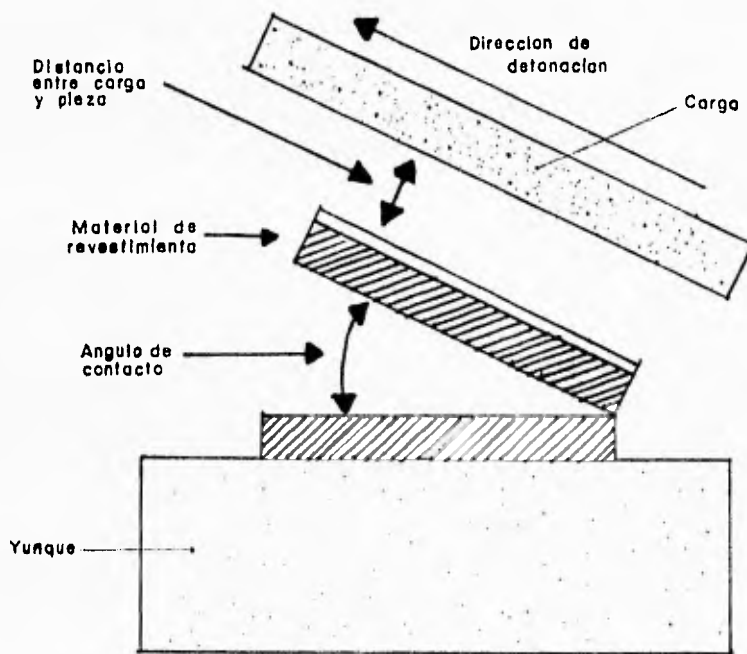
Soldadura por explosión (EXW)
